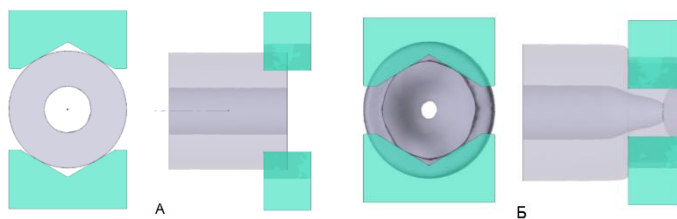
Моделювання кування циліндра з наскрізним отвором, А – початкова заготовка, Б – поковка
